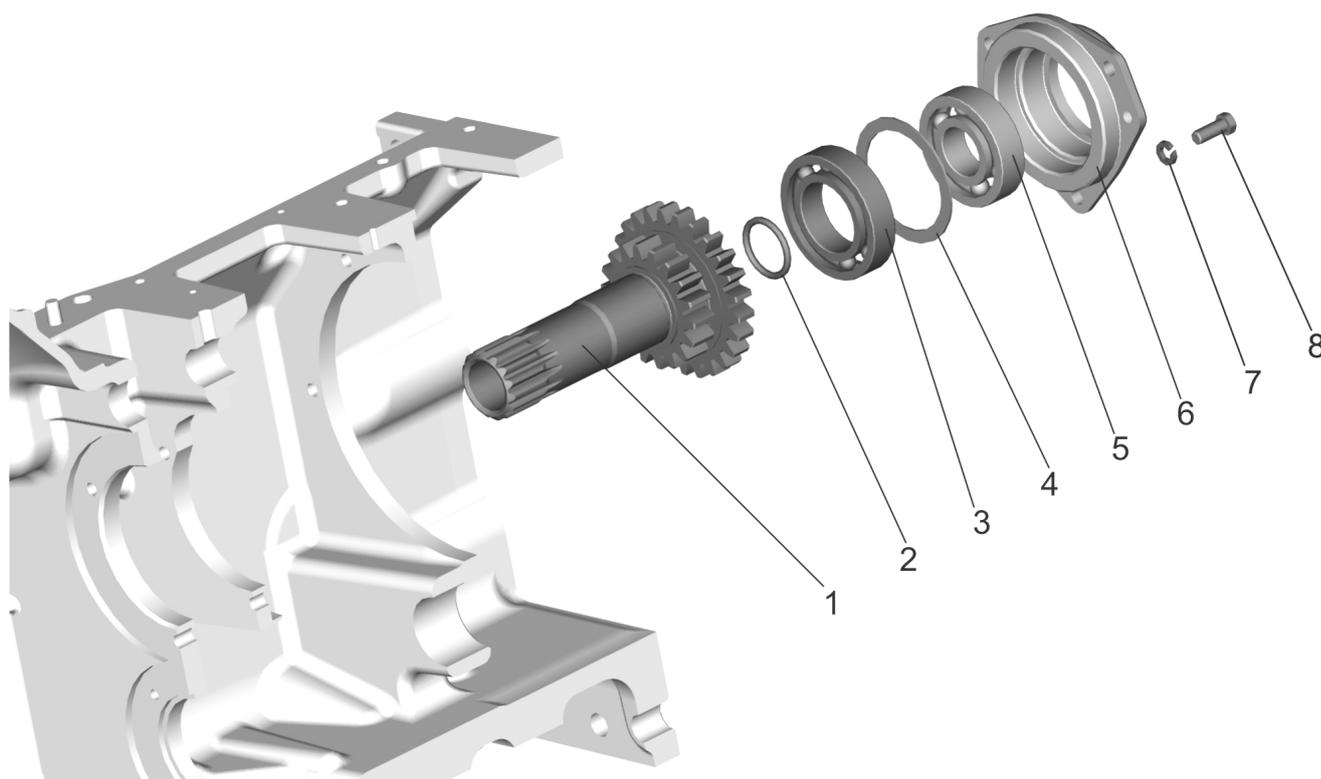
Корпус сцепления. Привод ВОМ. ($n_{дв}=2200$ об/мин)
